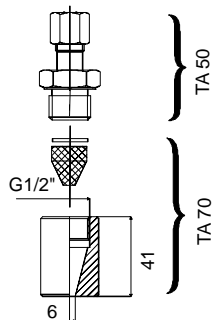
TA 70 Einschweißverschraubung für Lebensmittelanwendung (für TA 50)
